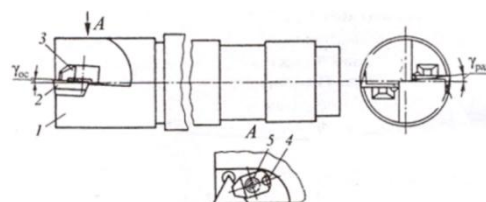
Концевая фреза с однорядными пластинами
